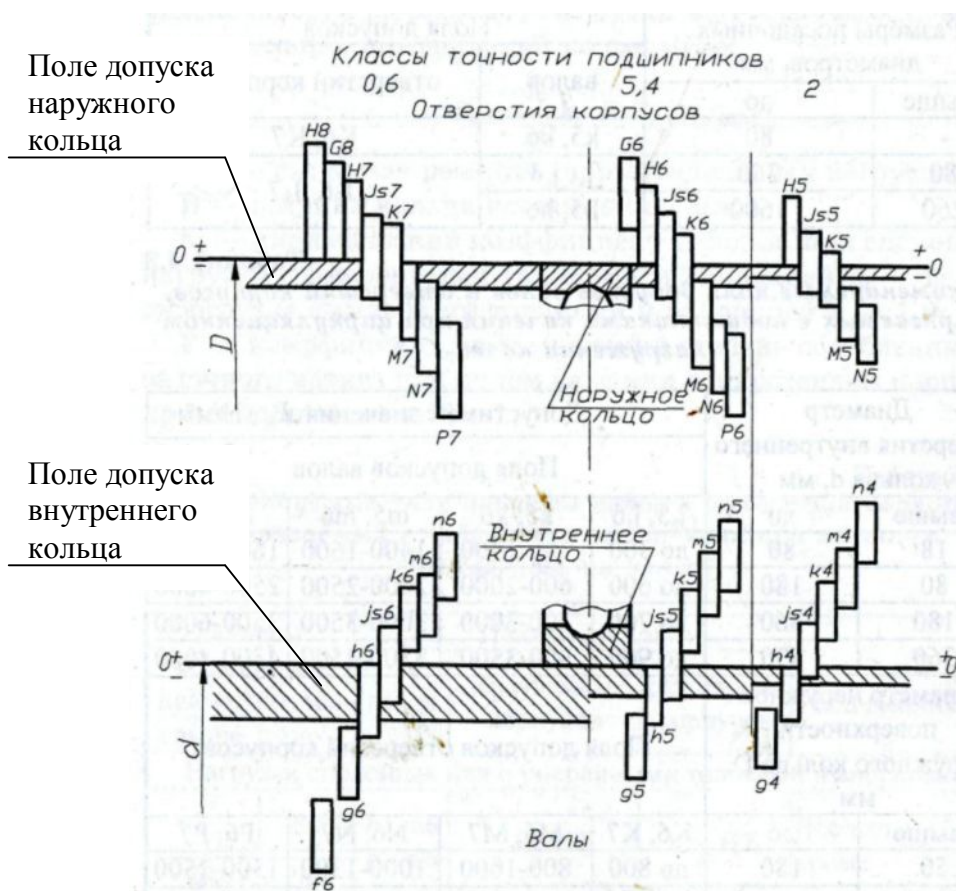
Схема расположения полей допусков колец подшипника качения, валов и отверстий в корпусе.
